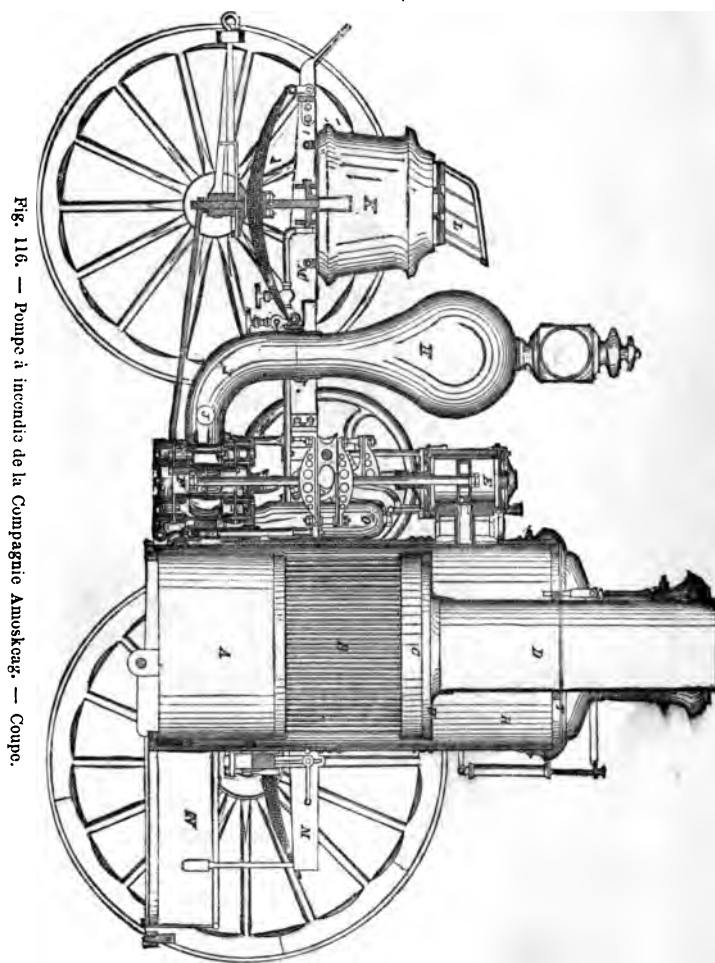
Pompe à incendie de la Compagnie Amuskeag. — Coupe.
